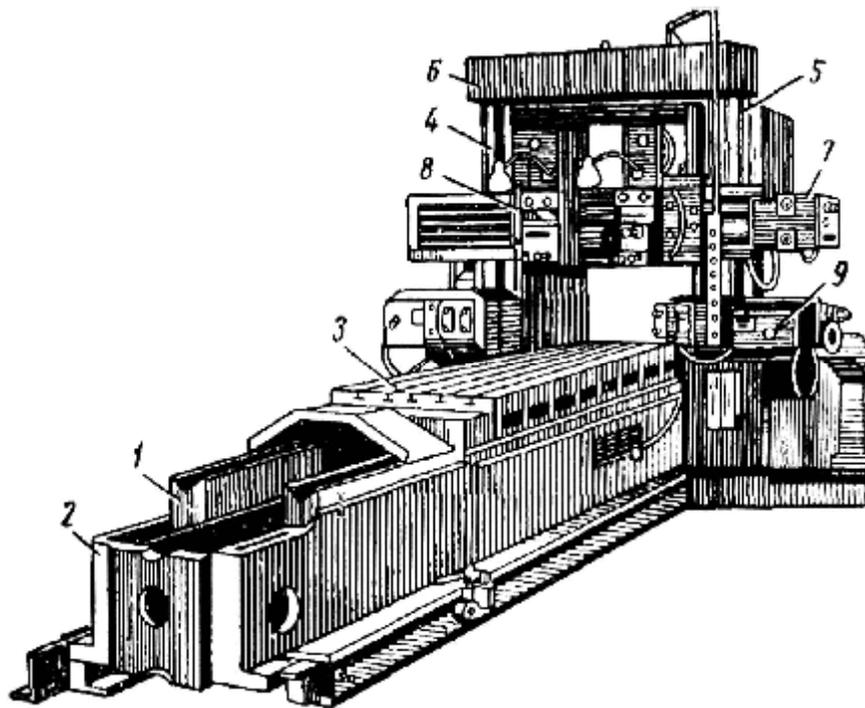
Станок продольно-фрезерный для обработки крупногабаритных деталей: 1, 2 элементы станины; 3 – стол; 4, 5 – стойки; 6 – поперечина; 7 – траверса; 8 – фрезерные головки с вертикальными шпинделями; 9 – фрезерные головки с горизонтальными шпинделями
